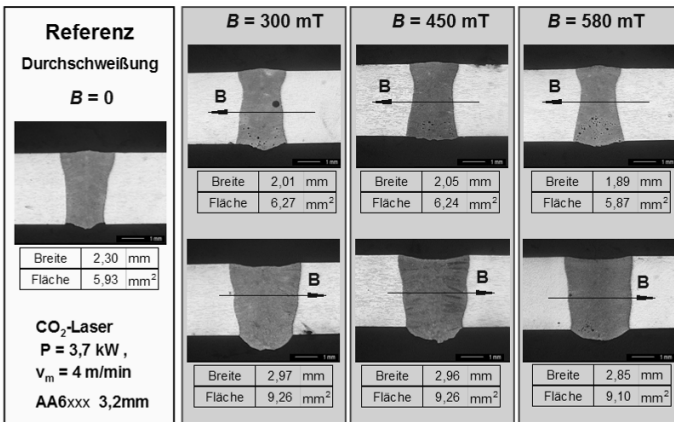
Veränderung des Nahtquerschnitts durch Anlegen eines externen Magnetfeldes beim CO₂-Lasersatrahlschweißen.
